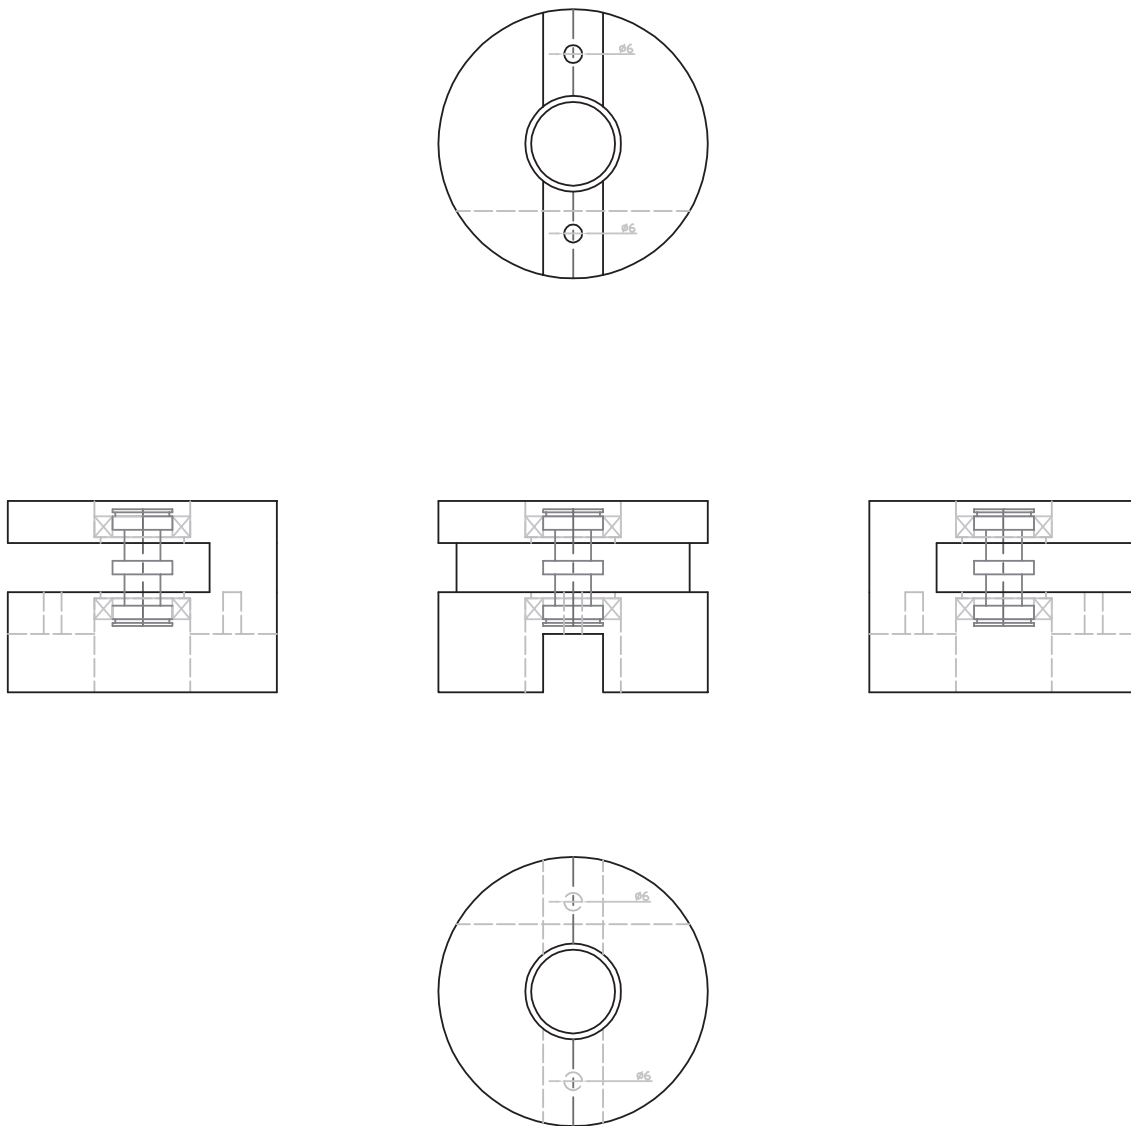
Ensemble coin inférieur+roulements+axe assemblé.
